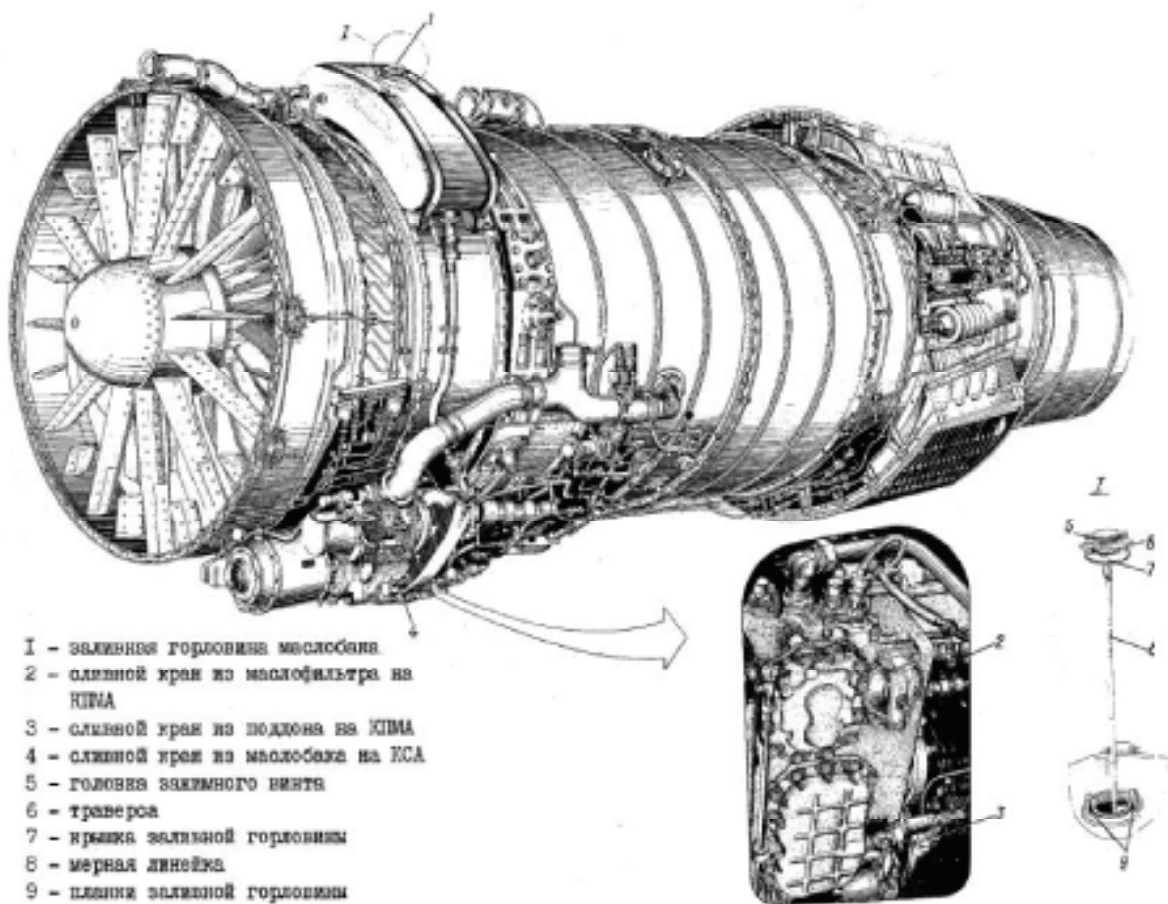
Общий вид размещения агрегатов на двигателе
